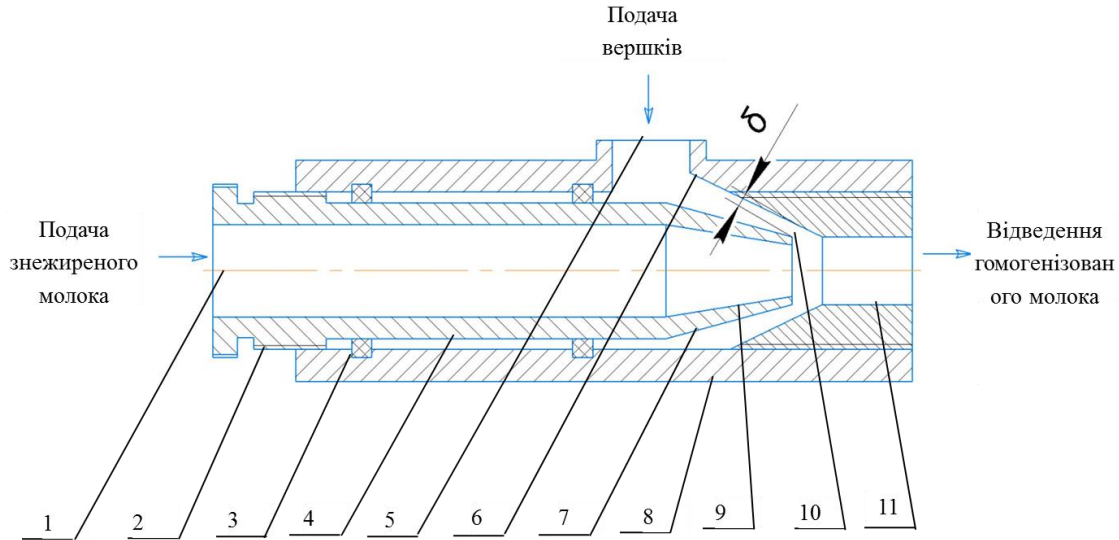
Струминно-щілинний гомогенізатор молока з роздільною подачею вершків: 1–центральный канал; 2–різьбова частина; 3–ущільнювачі; 4–конфузор; 5–патрубок; 6–внутрішня поверхня патрубку подачі вершків; 7–конфузор; 8–корпус; 9–конусний канал; 10–щілинний канал; 11–дифузор
